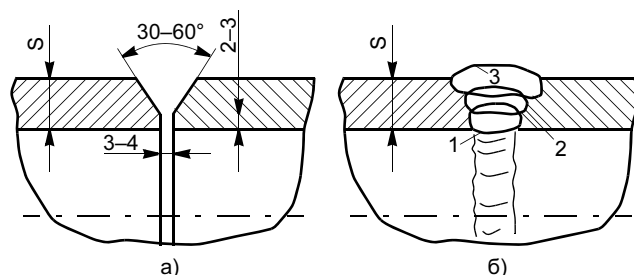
Рекомендуемое выполнение подварочного шва в сквозную местную выборку соединения (поперечное сечение): а — форма и размеры выборки после удаления поврежденного металла; б — очередность многослойного заполнения выборки расплавленным металлом при сварке
